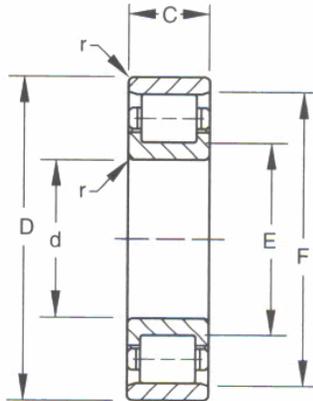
Dimensiones genérica Rodamiento cilíndrico.
